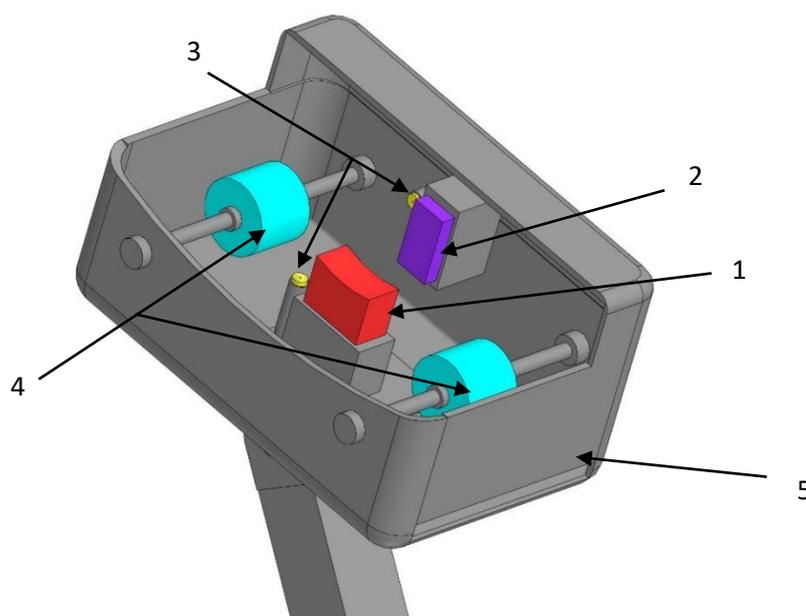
Пример установки роботизированного прибора неразрушающего контроля бандажей колесных пар на позиции обточки
